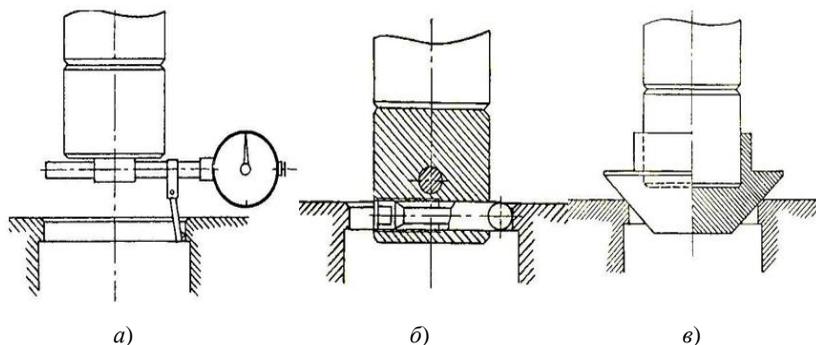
Устройства для обеспечения соосности осей шпинделя станка и отверстия цилиндра:
